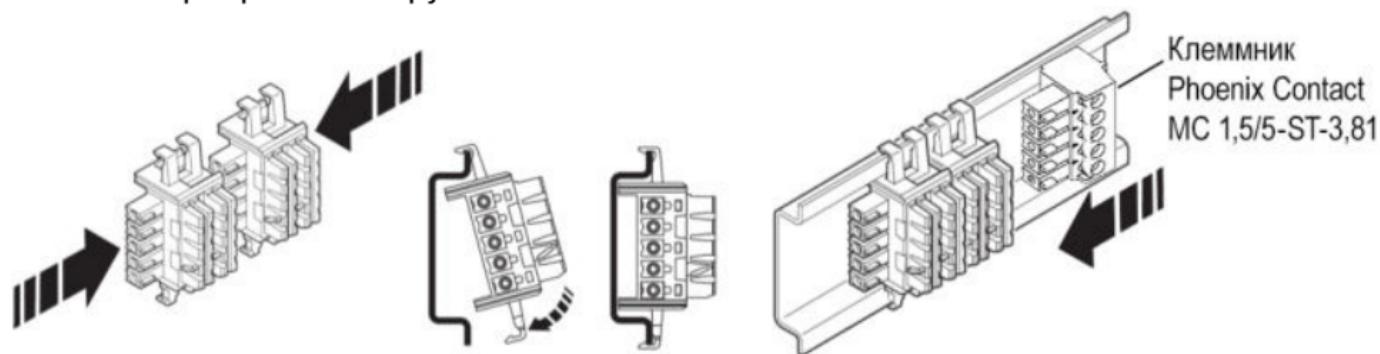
Установка шинных соединителей на DIN- рейку
